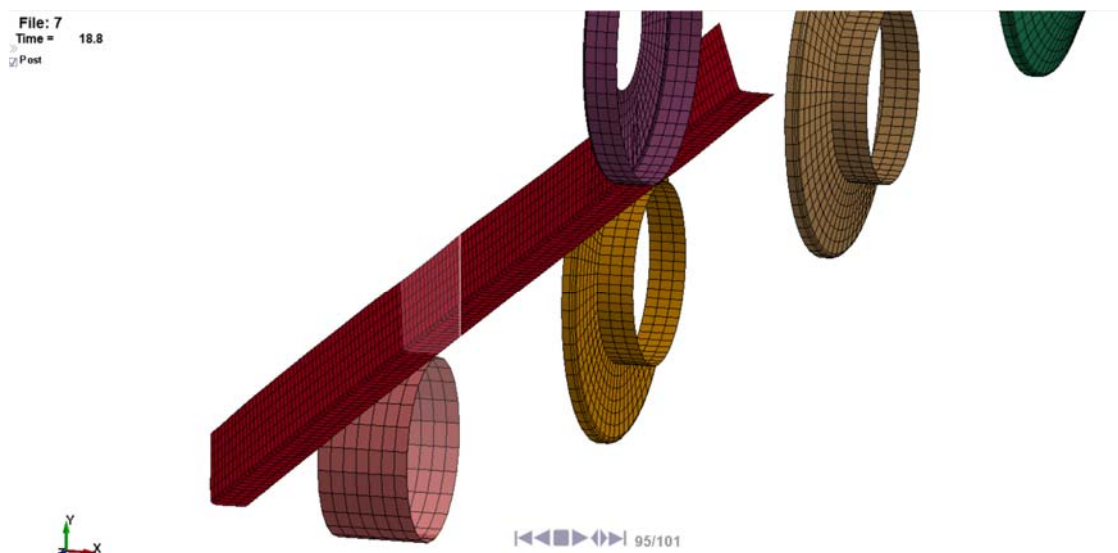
Внешний вид профиля и расположение контрольного сечения
